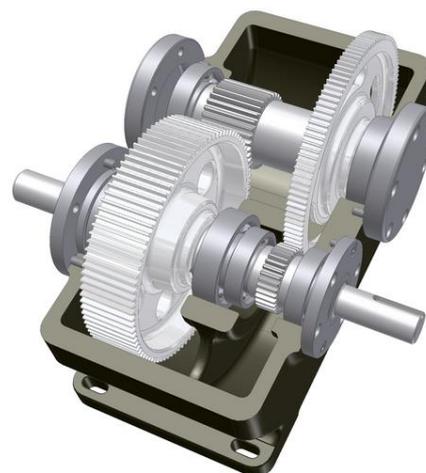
Пространственная модель цилиндрического двухступенчатого соосного редуктора
